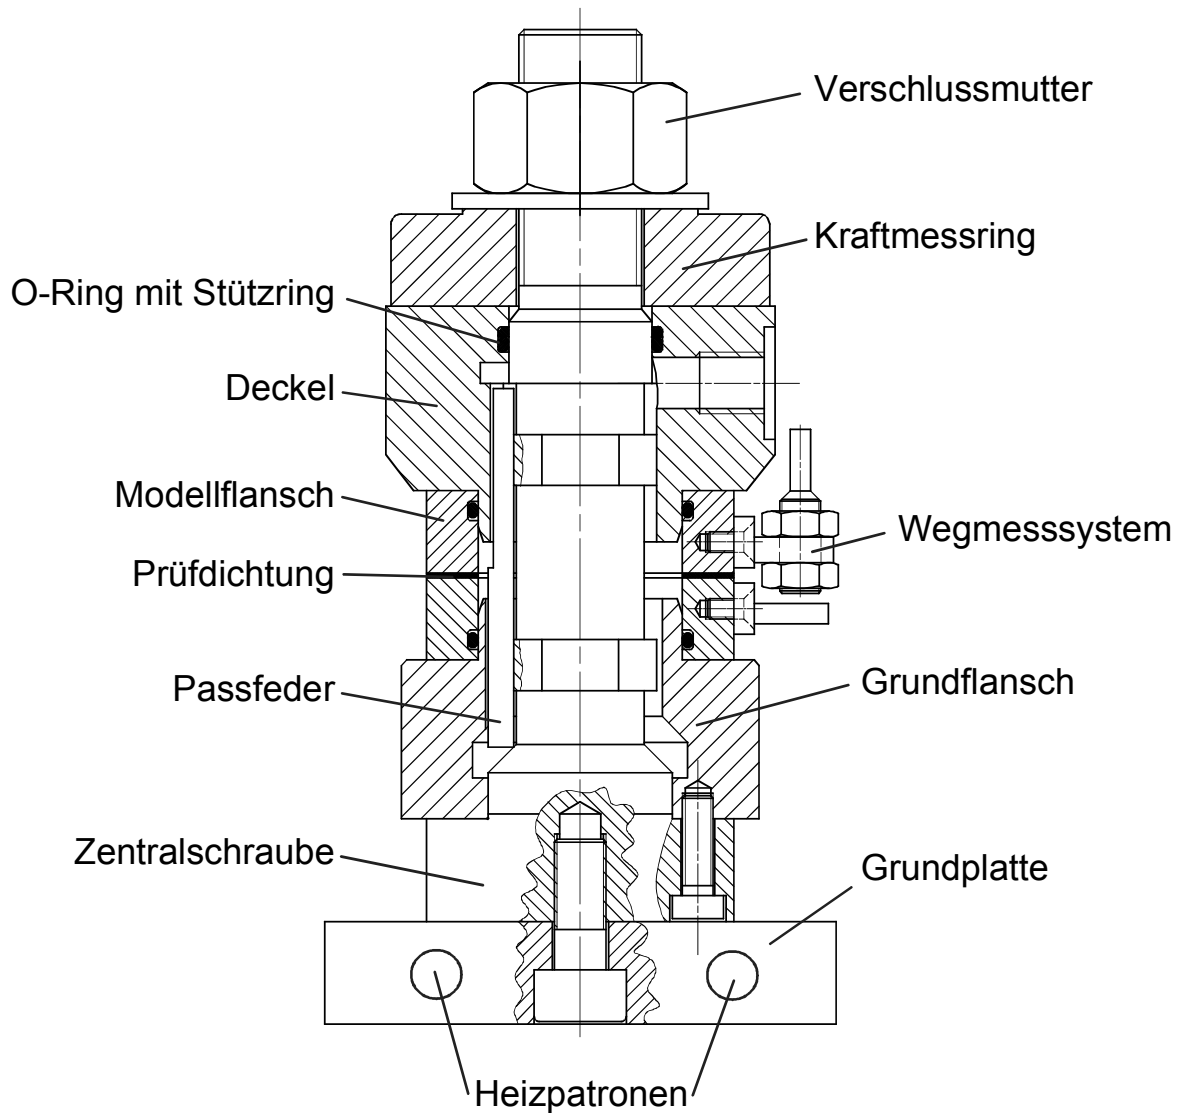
Zusammenbauzeichnung des Innendruckprüfstandes (IP)
